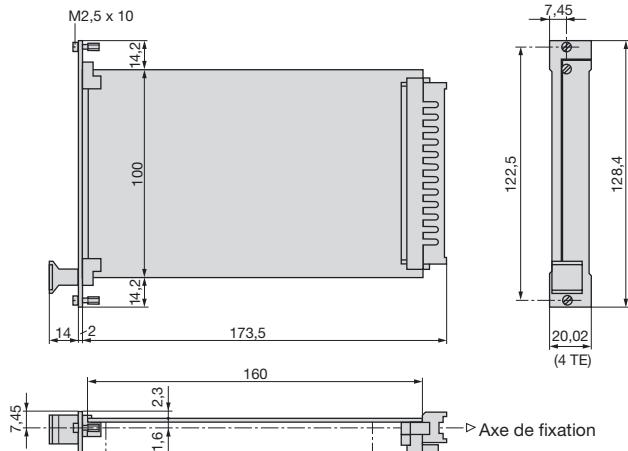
EURAX B 811, largeur de la plaque frontale 4 TE.
